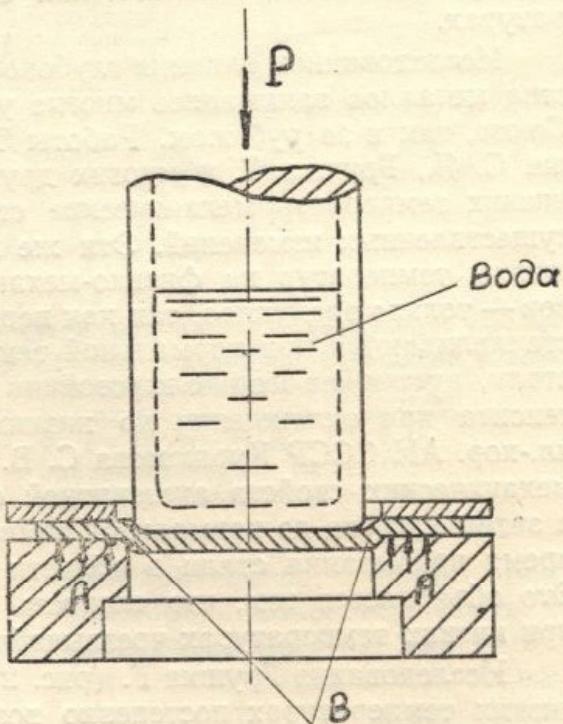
А — подвод тепла; В — зона разрушения деталей.
